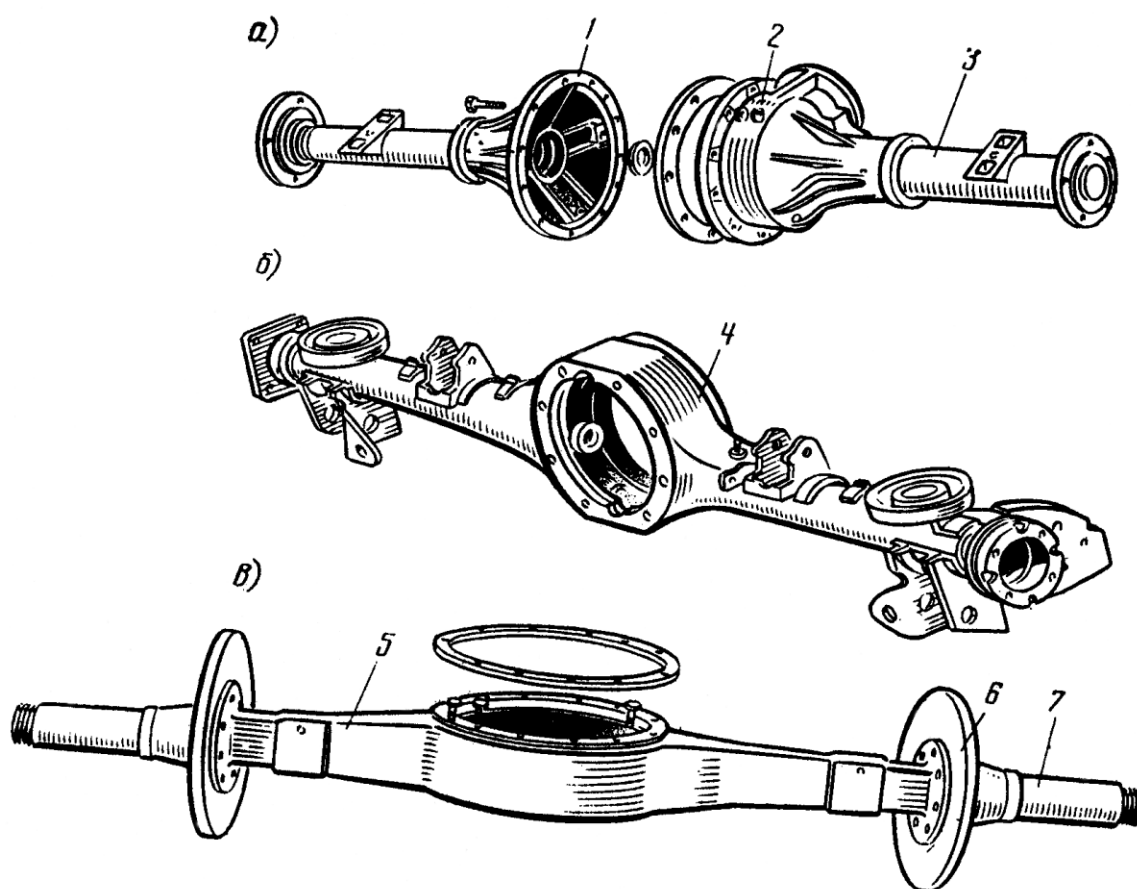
Ведущие мосты: а) – разъемный, б) – неразъемный штампованно-сварной, в) – неразъемный литой: 1 и 2 – литые части, соединяемые болтами, 3 – трубчатые кожухи полуосей, 4 – балка рубчатой формы с развитой центральной частью, 5 – балка прямоугольного сечения, 6 – диски, 7 – трубы
